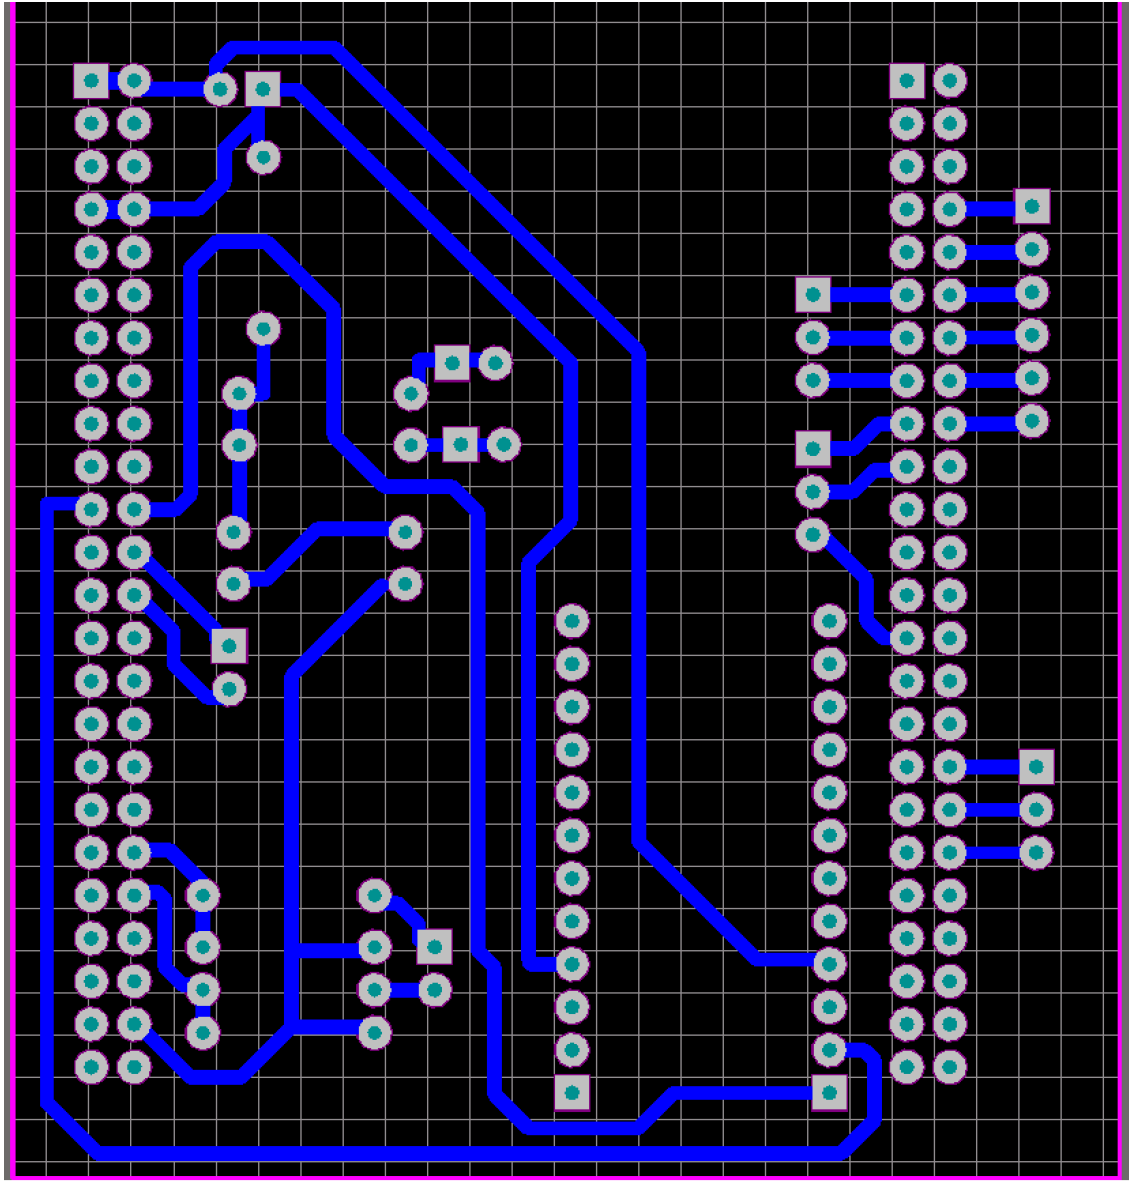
Shiel PCB para Tarjeta Beaglebone Black de prototipo Kay Juul H.
